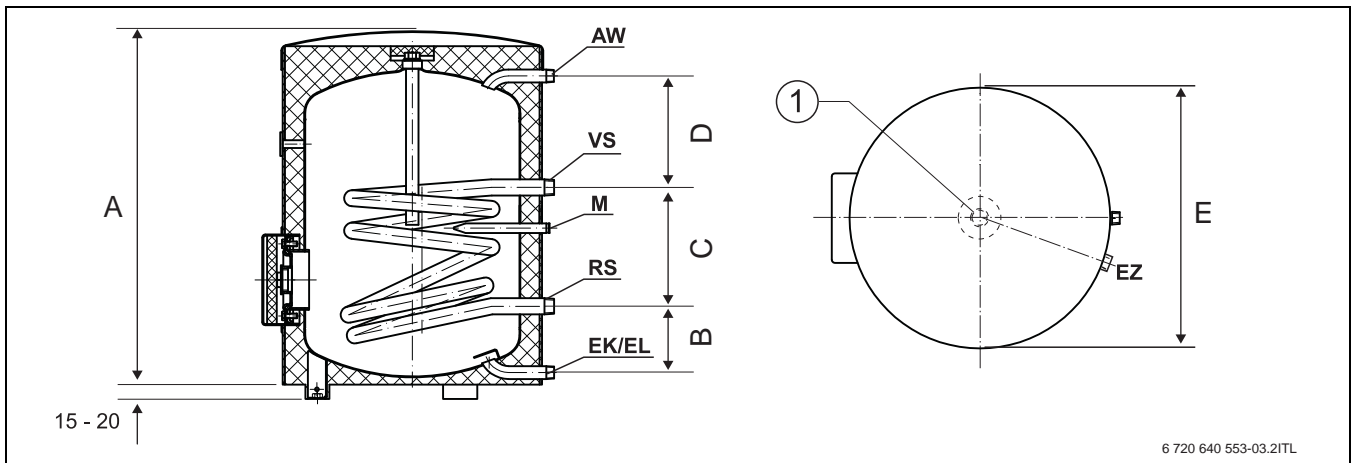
Dimensiones y conexiones Storacell S75-90 ZB-solar
